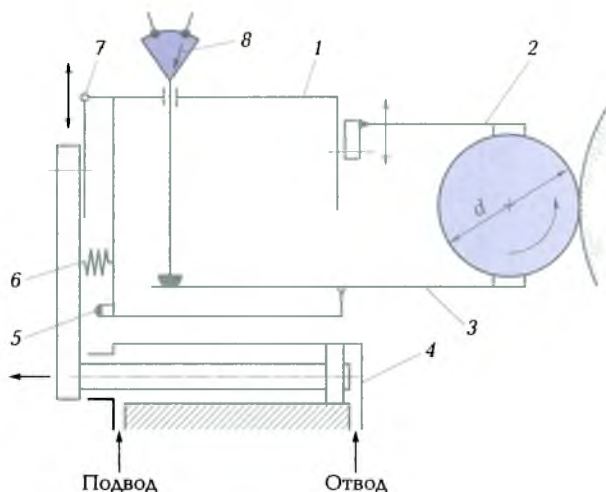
Двухконтактный прибор с одним измерительным рычагом:
